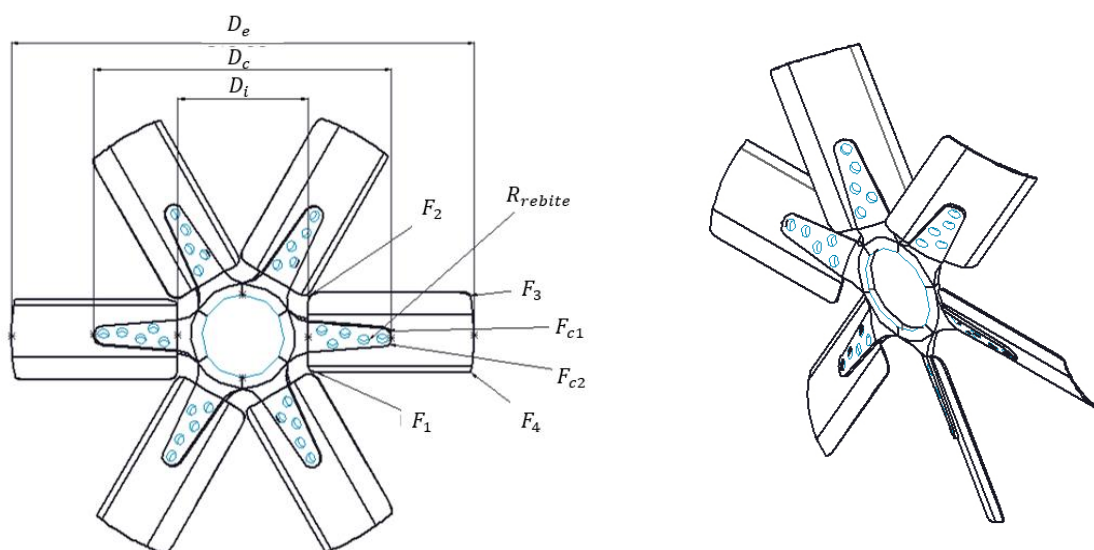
Esquema da vista transversal e do isométrico do rotor axial
